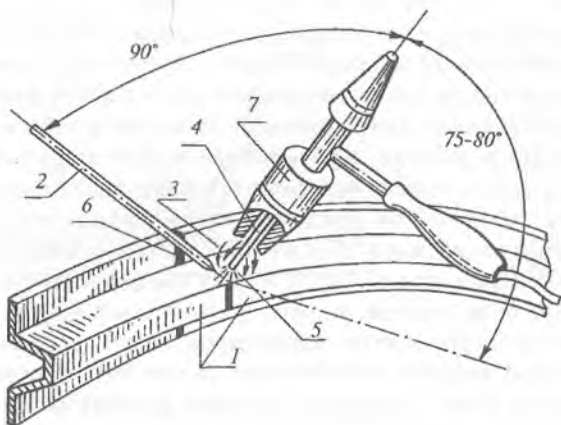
Ручная аргоно-дуговая сварка: 1 — свариваемые детали; 2 — присадочный материал; 3 — струя аргона; 4 — вольфрамовый электрод; 5 — дуга; 6 — сварной шов; 7 — горелка с каналом для аргона
